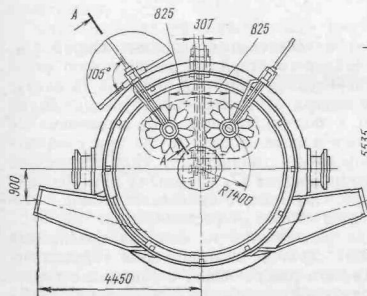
Сталеразливочный сварной ковш вместимостью 480 т
